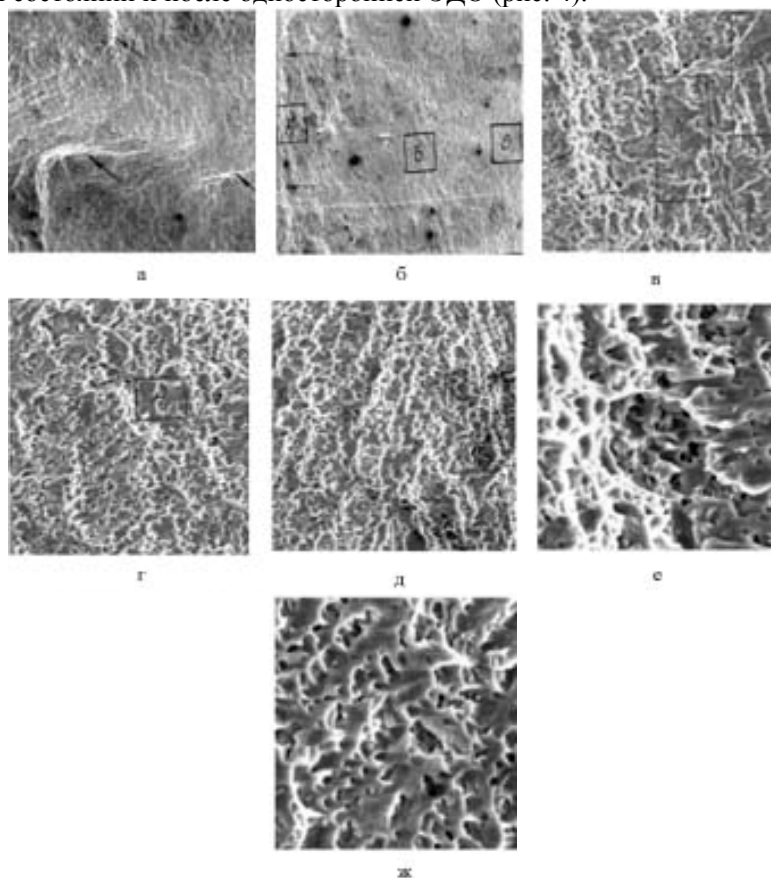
Общий вид изломов сварных соединений сплава АМг5, полученных при разрушении образцов:
